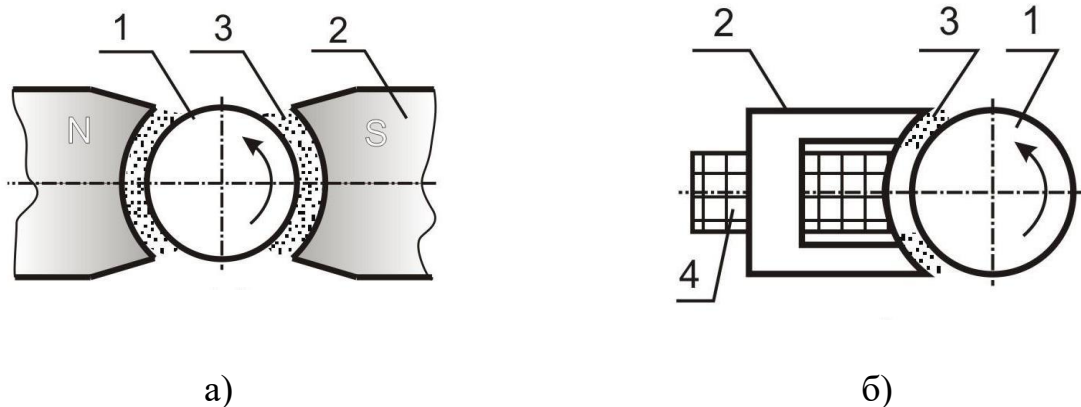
Схема МАО циліндричних деталей: а) з розташуванням електромагнітних індукторів (ЕМІ) з двох сторін; б) з розташуванням ЕМІ з однієї сторони оброблюваної деталі: 1 – заготовка, 2 – полюс, 3 – абразивний порошок, 4 – магнітна котушка
